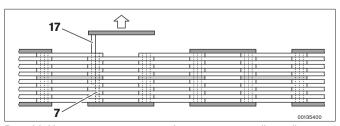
Удалить коренную цапфу с соединенной с ней сварочной пластиной
